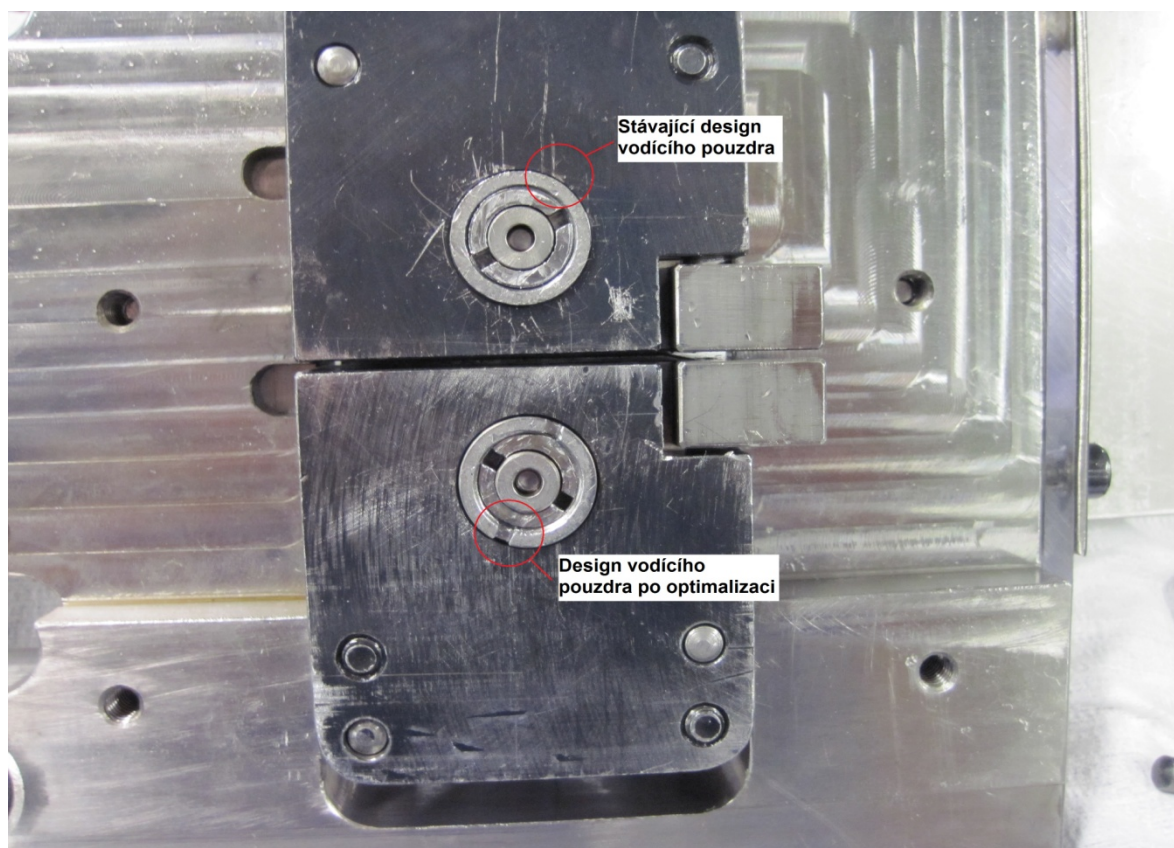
3 Vodící pouzdro a místo vzniku deformace.
